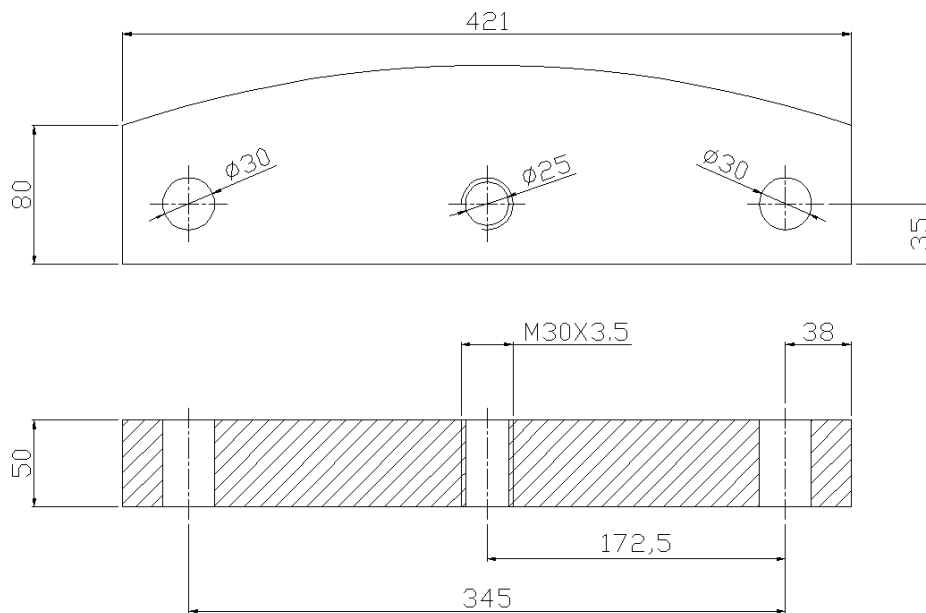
PLANO DE PLACA SEPARADORA DE BARRAS FIJAS
